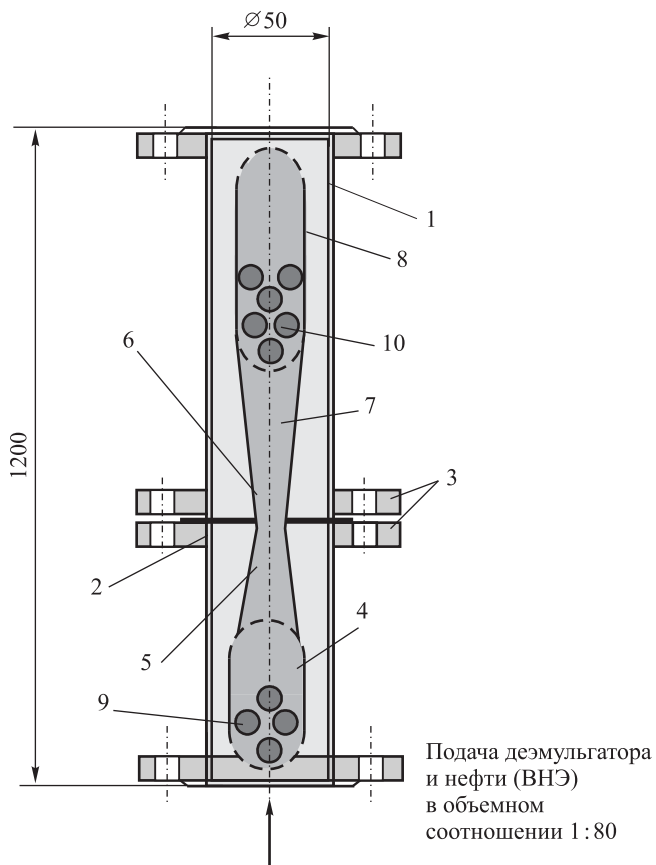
Кавитационно-ультразвуковой диспергатор: 1 — корпус; 2 — диафрагма; 3 — фланцы; 4 — смеситель конфузора; 5 — конфузور; 6 — горловина; 7 — диффузор; 8 — смеситель диффузора; 9 — подвижная насадка смесителя конфузора; 10 — подвижная насадка смесителя диффузора
